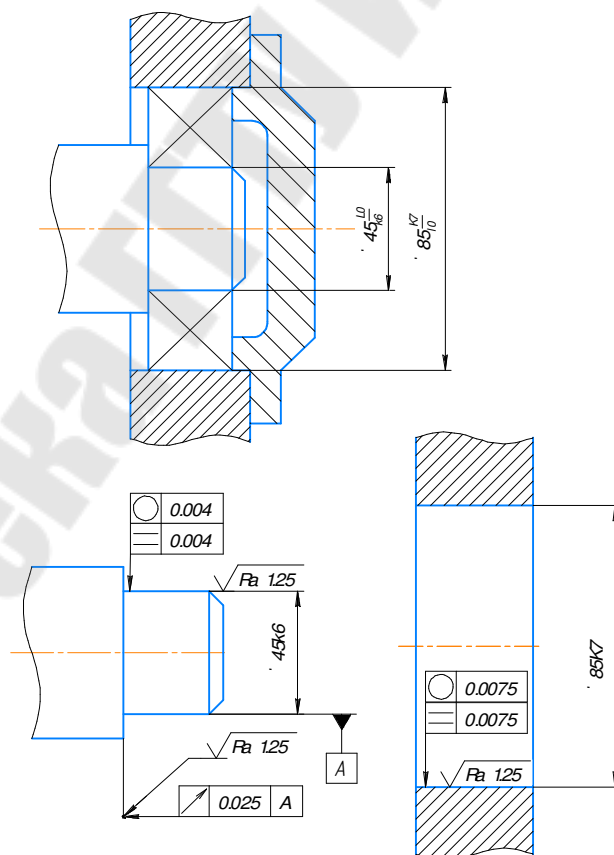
Эскиз подшипникового узла и деталей, входящих в него
